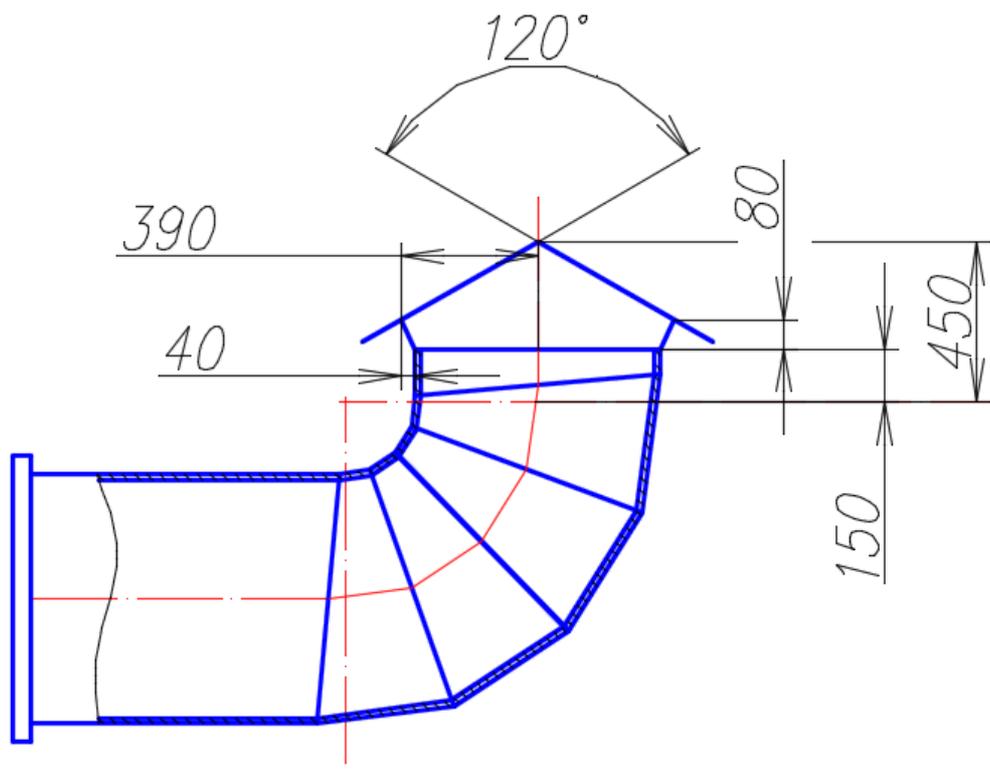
Чертеж трубы для подачи загрязненного воздуха
